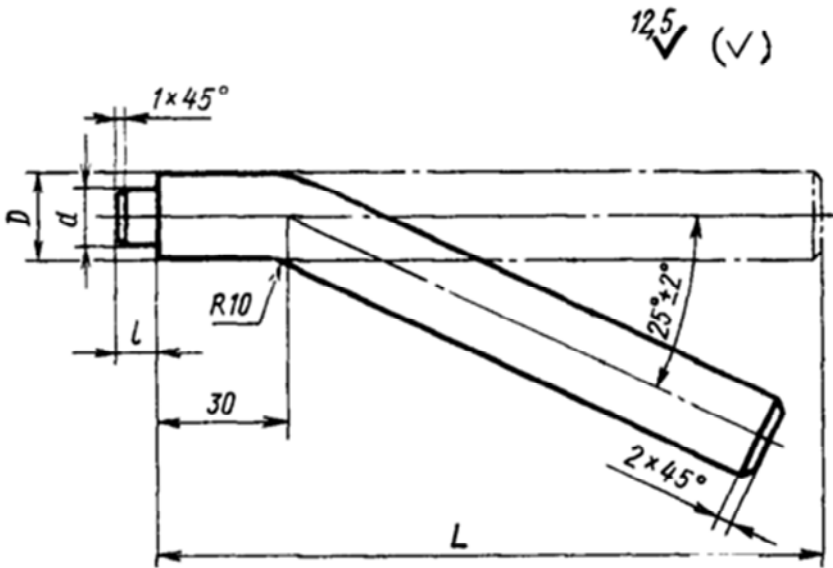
Конструкция рукоятки эксцентрикового замка
